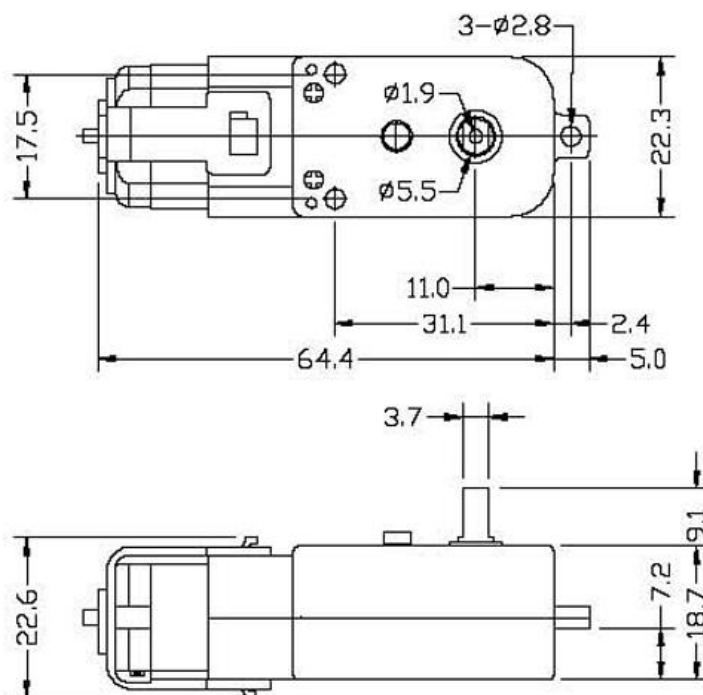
Зовнішній вигляд двигуна постійного струму з редуктором
